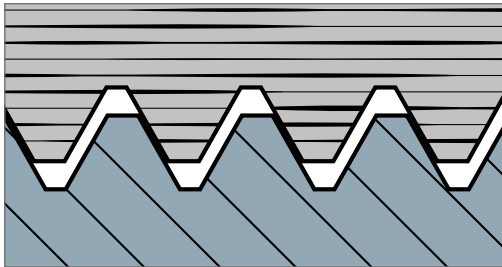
Gewinde nach DIN 7500 Ausführung Form Duo
